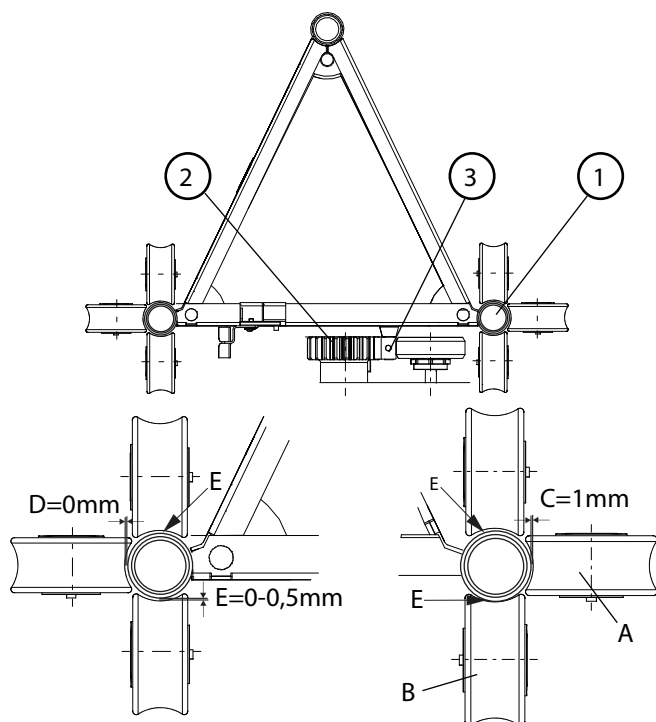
Угловая труба мачты (1), зубчатое колесо (2), зубчатая рейка (3)
